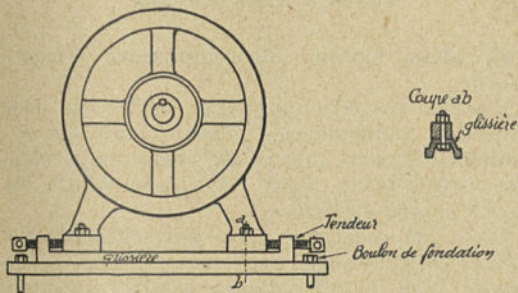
Montage d'une machine sur glissières et tendeurs.
